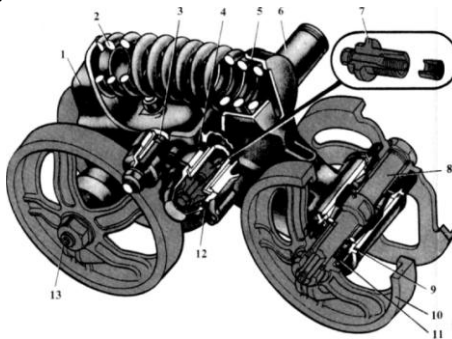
Опорні котки з пружною балансирною підвіскою (каретка) (ДТ-75МЛ): 1,5 - балансири; 2 - пружина; 3,8 - вісі; 4,12,13 - пробки; 6 - цапфа; 7 - гайка; 9 прокладка; 10 - коток; 11 – ущільнювач.
